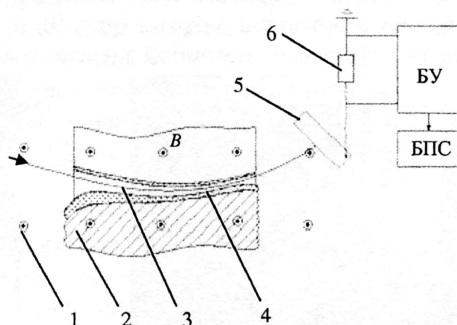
Схема регулирования кривизны электронного пучка и канала проплавления по величине проходящего тока: 1 – вектор индукции магнитного поля; 2 – свариваемые изделия; 3 – электронный пучок; 4 – сварочная ванна; 5 – коллектор приема проходящего тока; 6 – шунт. БУ – блок управления, БПС – блок питания соленоида
